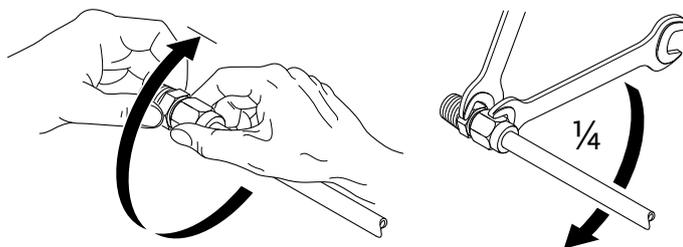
Дополнительный поворот резьбового соединения с обжимным кольцом на 1/4 оборота
